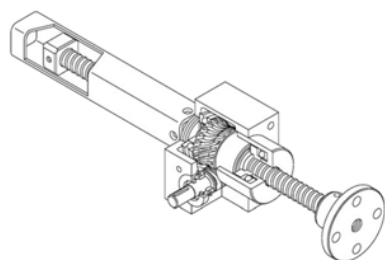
Kugelgewindespindel in verdrehgesicherter Ausführung
